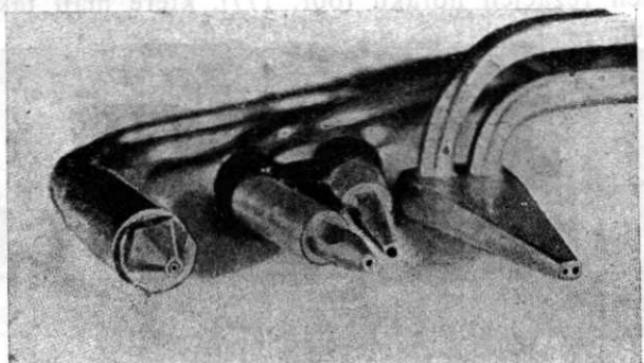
Rez hlavou řezacího hořáku se soustřednými dýzami.
